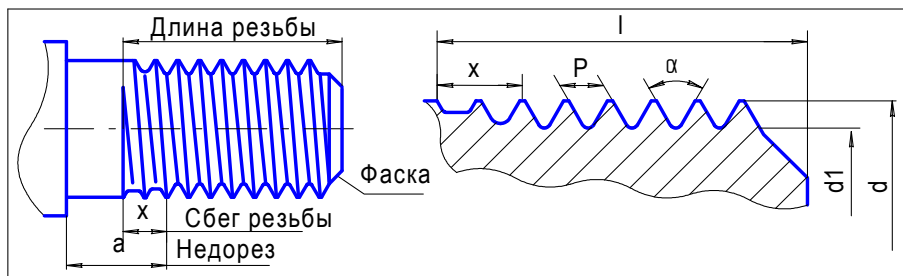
Конструктивные элементы и параметры цилиндрической резьбы
